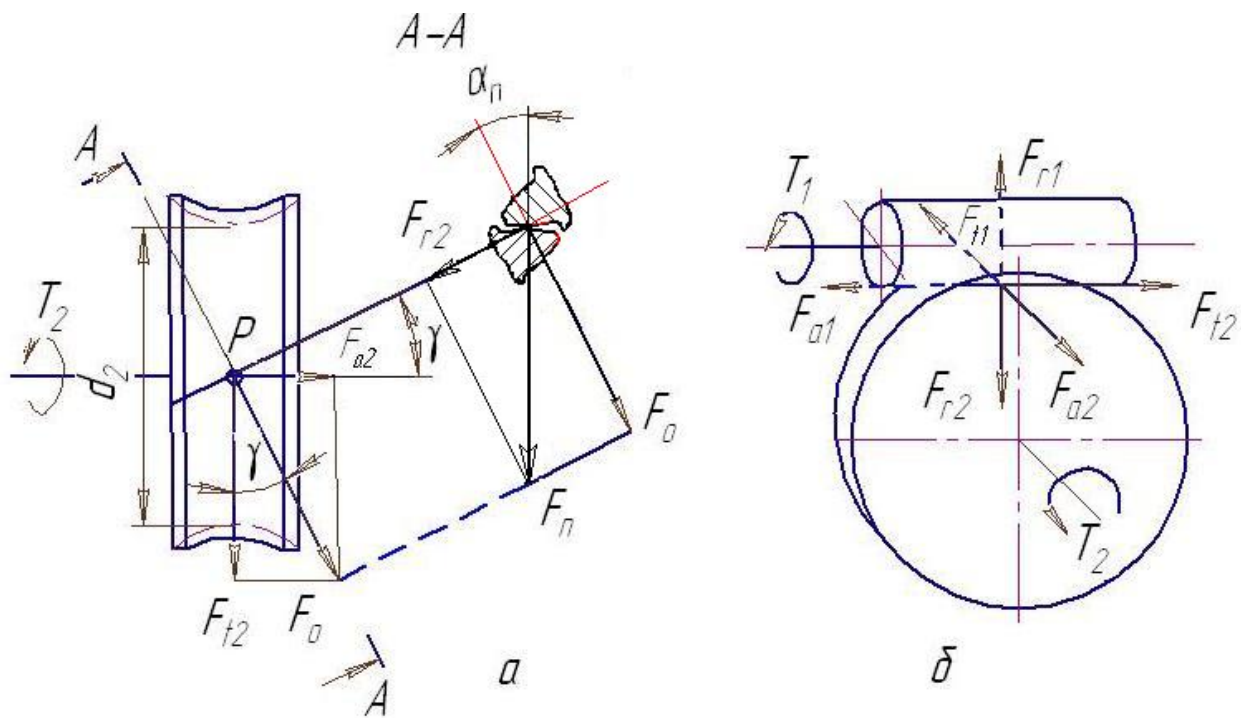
Зусилля на зубці черв'ячного колеса(а) і витки черв'яка (б)
